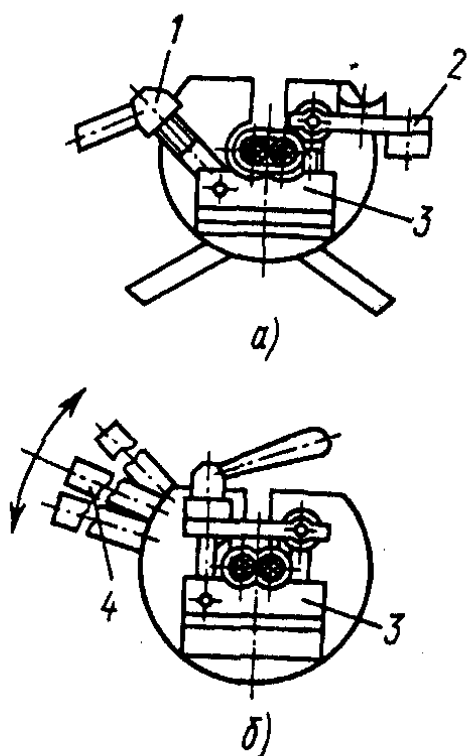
Заушные узлы приспособления МИ-189А:
